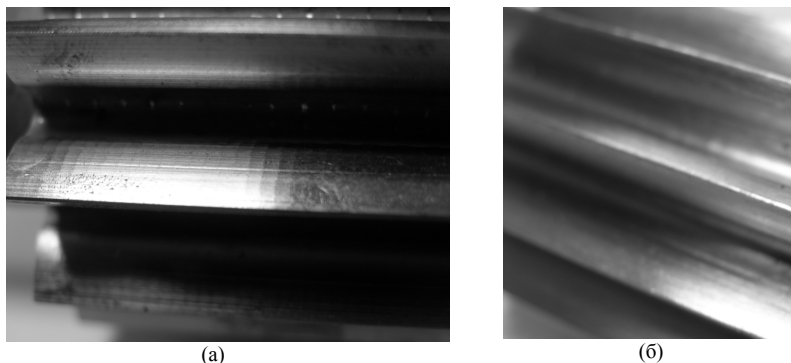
Поверхня зубчастого колеса до та після обробки алмазним зубохонінгуванням
